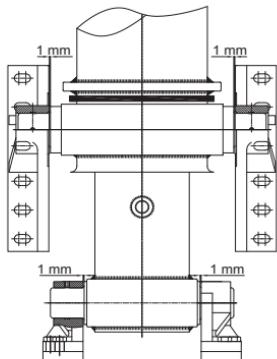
C Tipi Üçgen Braket Bağlantısı - Boşluk Gösterimi • Picture 18 - C Type Triangle Bracket Connection - Clearance Display
